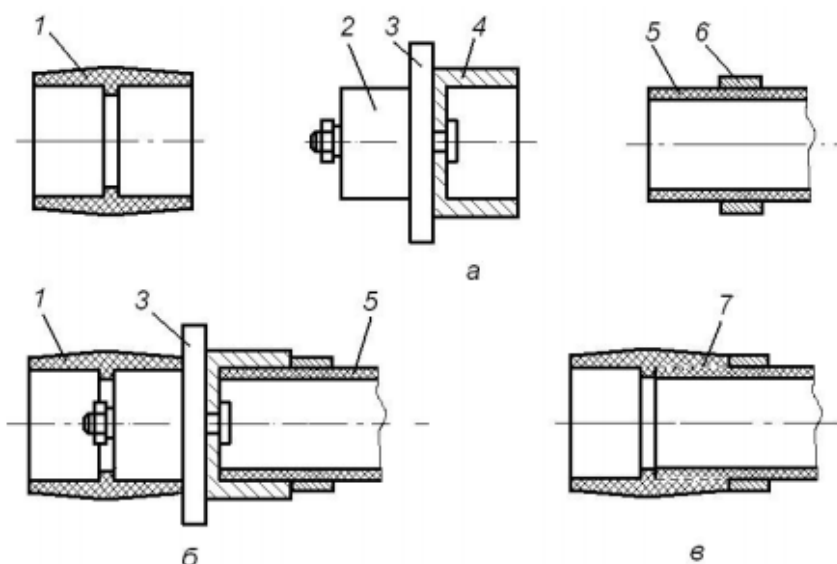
Схема сварки внахлест: а – нагреватель и стыкуемые детали; б – нагрев свариваемых поверхностей; в – сварное соединение трубы с муфтой; 1 – соединительный элемент; 2 – дорн; 3 – нагреватель; 4 гильза; 5 – труба; 6 – ограничительный хомут; 7 – сварной шов
